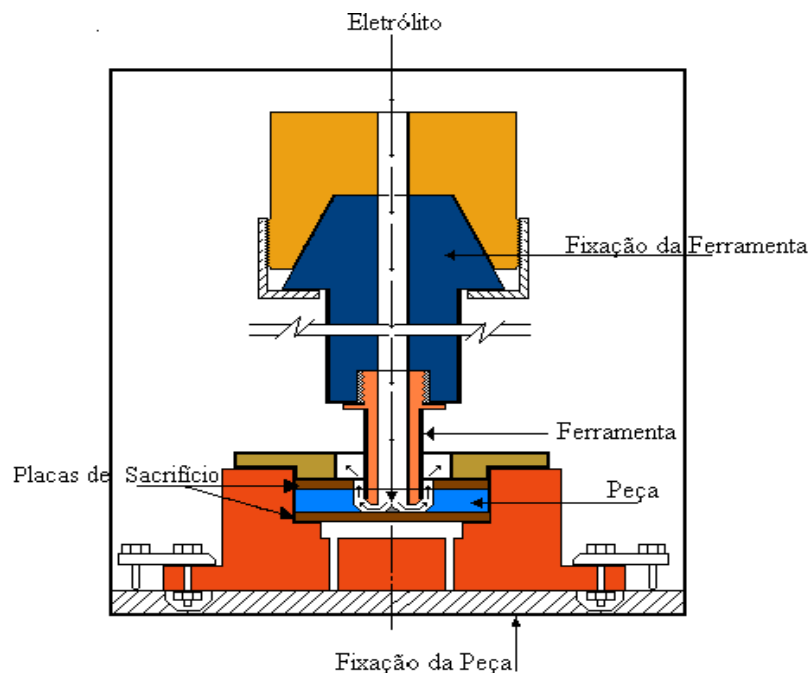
Vista em corte do ferramental de usinagem eletroquímica
